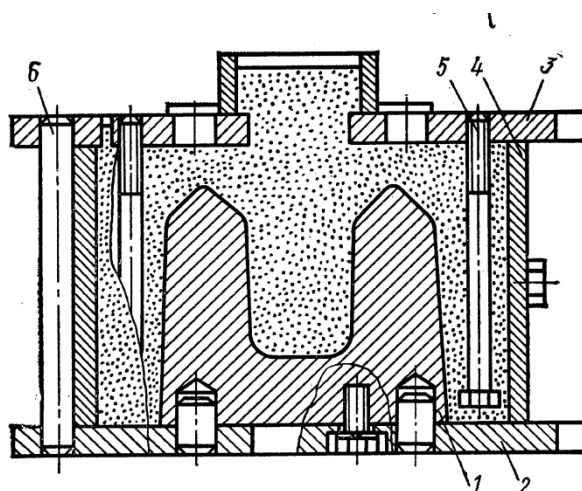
Форма для изготовления абразивного мастер-инструмента
